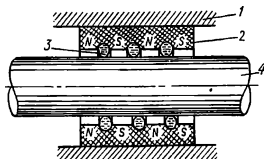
Магнитожидкостное уплотнение немагнитного вала: 1 — корпус; 2 — эластичный магнит; 3 — магнитная жидкость; 4 — вал из немагнитного материала
